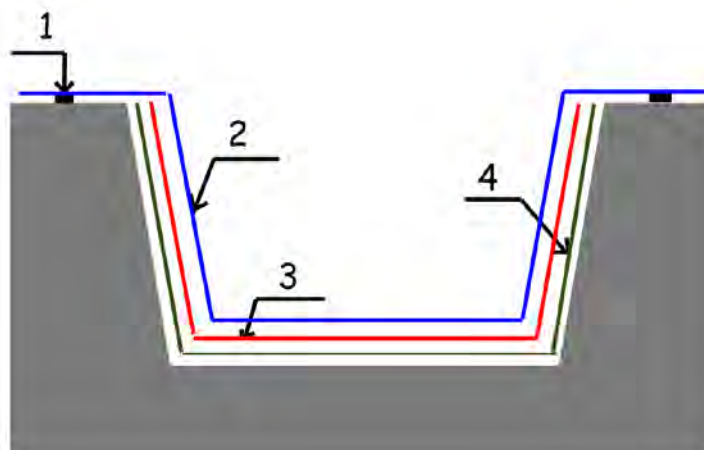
Процесс изготовления углепластиков прессованием или «мокрым» способ: 1- уплотнительная лента; 2 - вакуумный мешок; 3 - сухой армирующий материал; 4 - смола с введенным катализатором в виде полутвердой пленки
